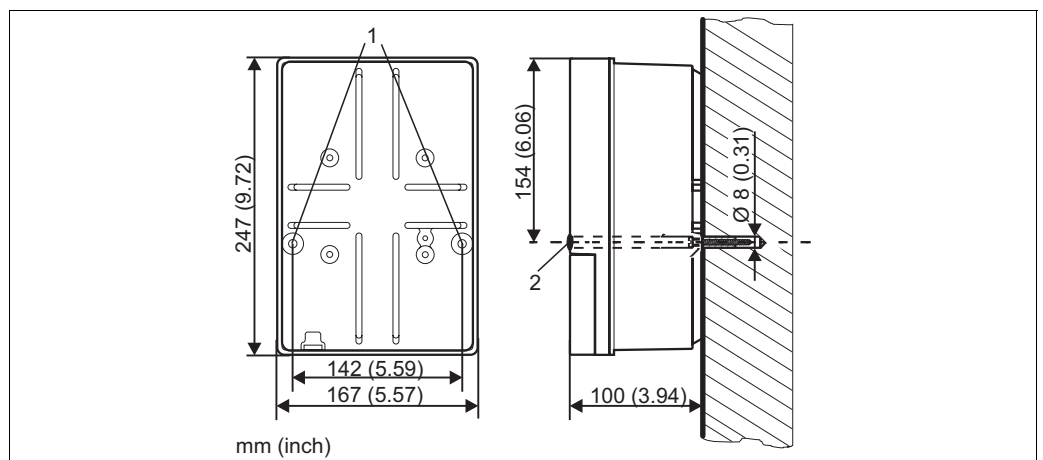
Maße für die Wandmontage, Befestigungsschraube: Ø 6 mm (0,24"), Dübel: Ø 8 mm (0,31")
